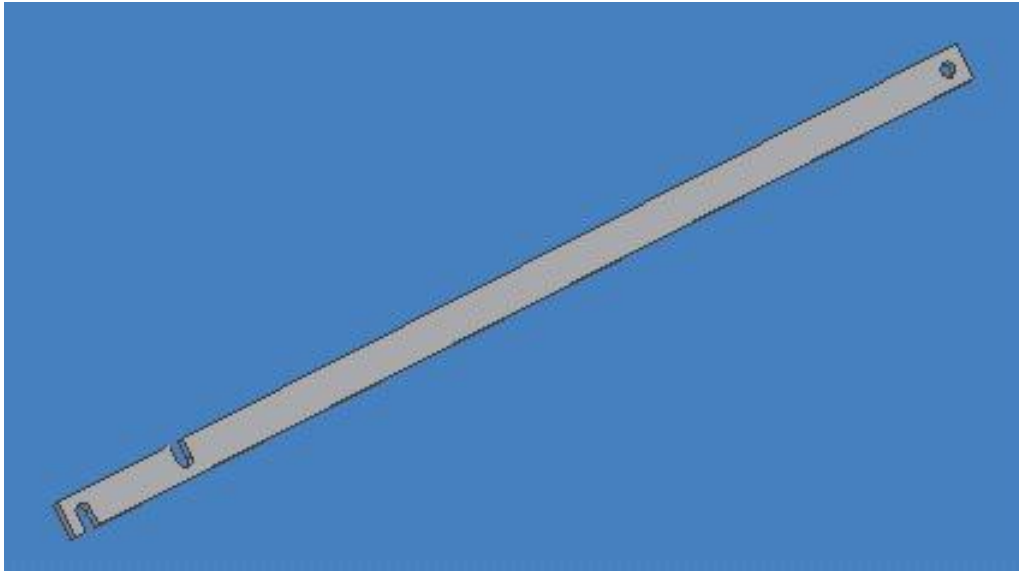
Pieza B1 . Perforaciones aplicadas a 24 piezas según el plano AND00 - 1000
